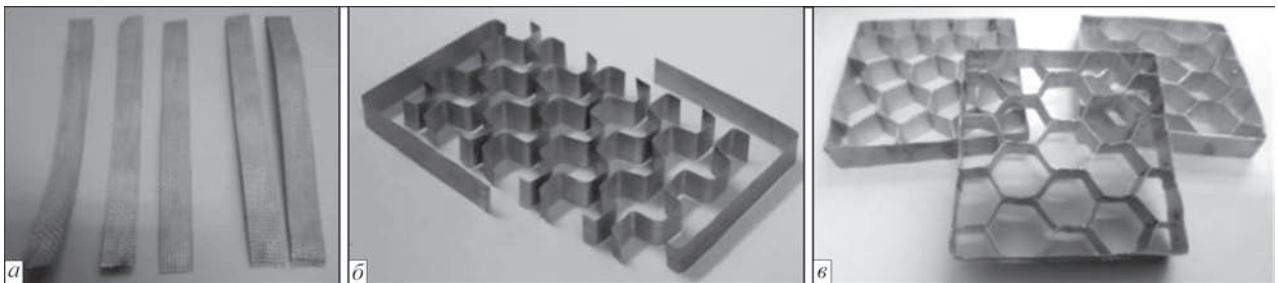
Етапи виготовлення стільникового заповнювача: а – стрічки з біметалевого матеріалу Al–Ti; б – заготовки профільованих стрічок для точкового зварювання стільникового заповнювача; в – стільниковий заповнювач розміром 72×72 мм
